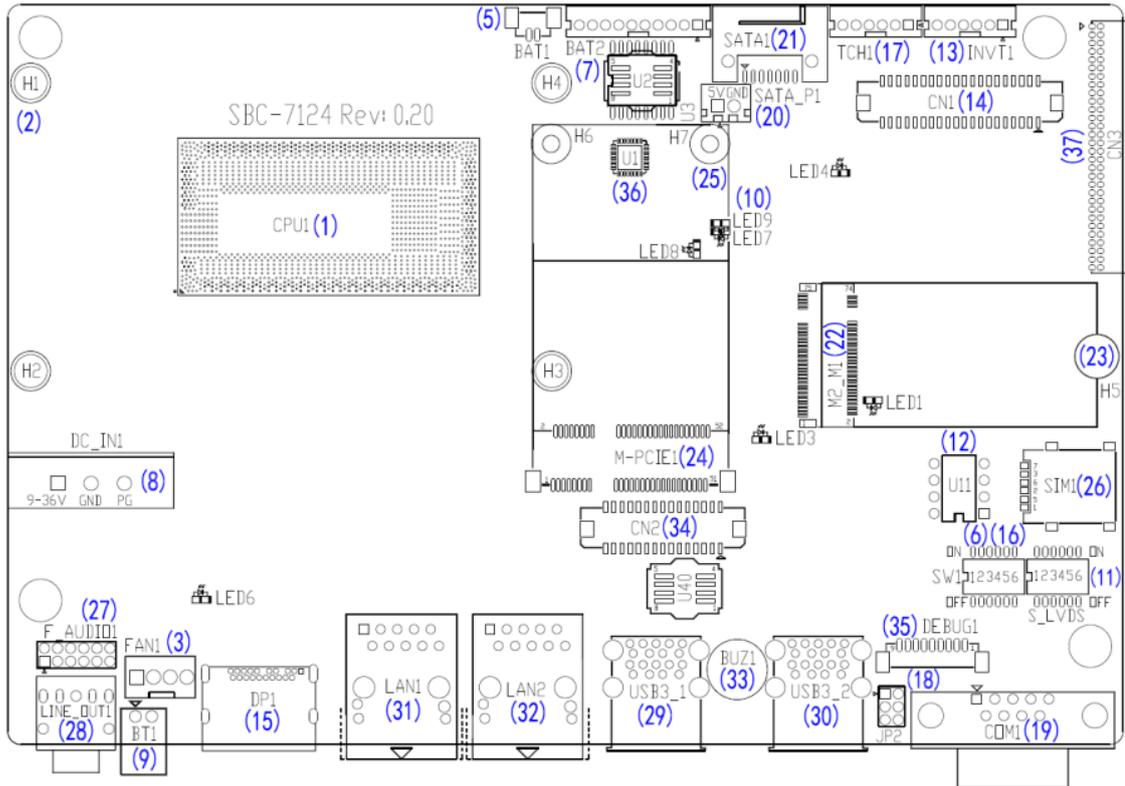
Jumper und Anschluss – Board Draufsicht
